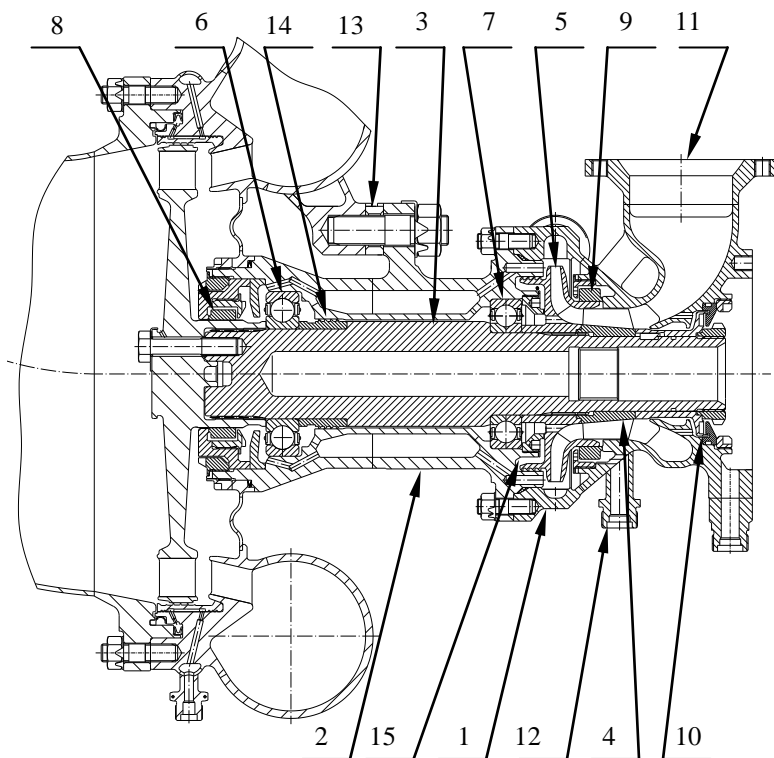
Насос аммиака с турбиной: 1 и 2 – корпуса; 3 – вал; 4 – шнек; 5 – крыльчатка; 6 и 7 – подшипники; 8 и 9 – плавающие кольца; 10 – импеллер; 11 – входной патрубок; 12 – штуцер отбора аммиака на охлаждение подшипника в ТНА окислителя; 13 – шпонка; 14 – лабиринтное уплотнение; 15 – полость автоматического разгрузочного устройства
